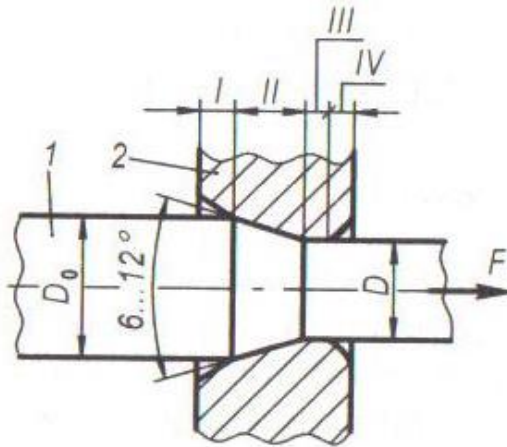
Схема волочиння: 1 – заготовка; 2 – волока; D і D_0 – діаметри до і після волочиння; F – зусилля волочиння
